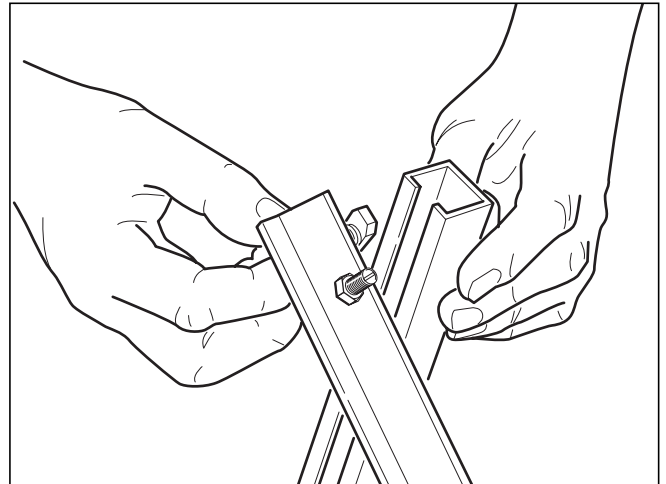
Constituer un triangle en joignant une cornière profilée et un rail de montage. Fixer le rail de montage selon l'angle d'appui (voir tab. 3.3). Scier toute partie dépassant éventuellement.
